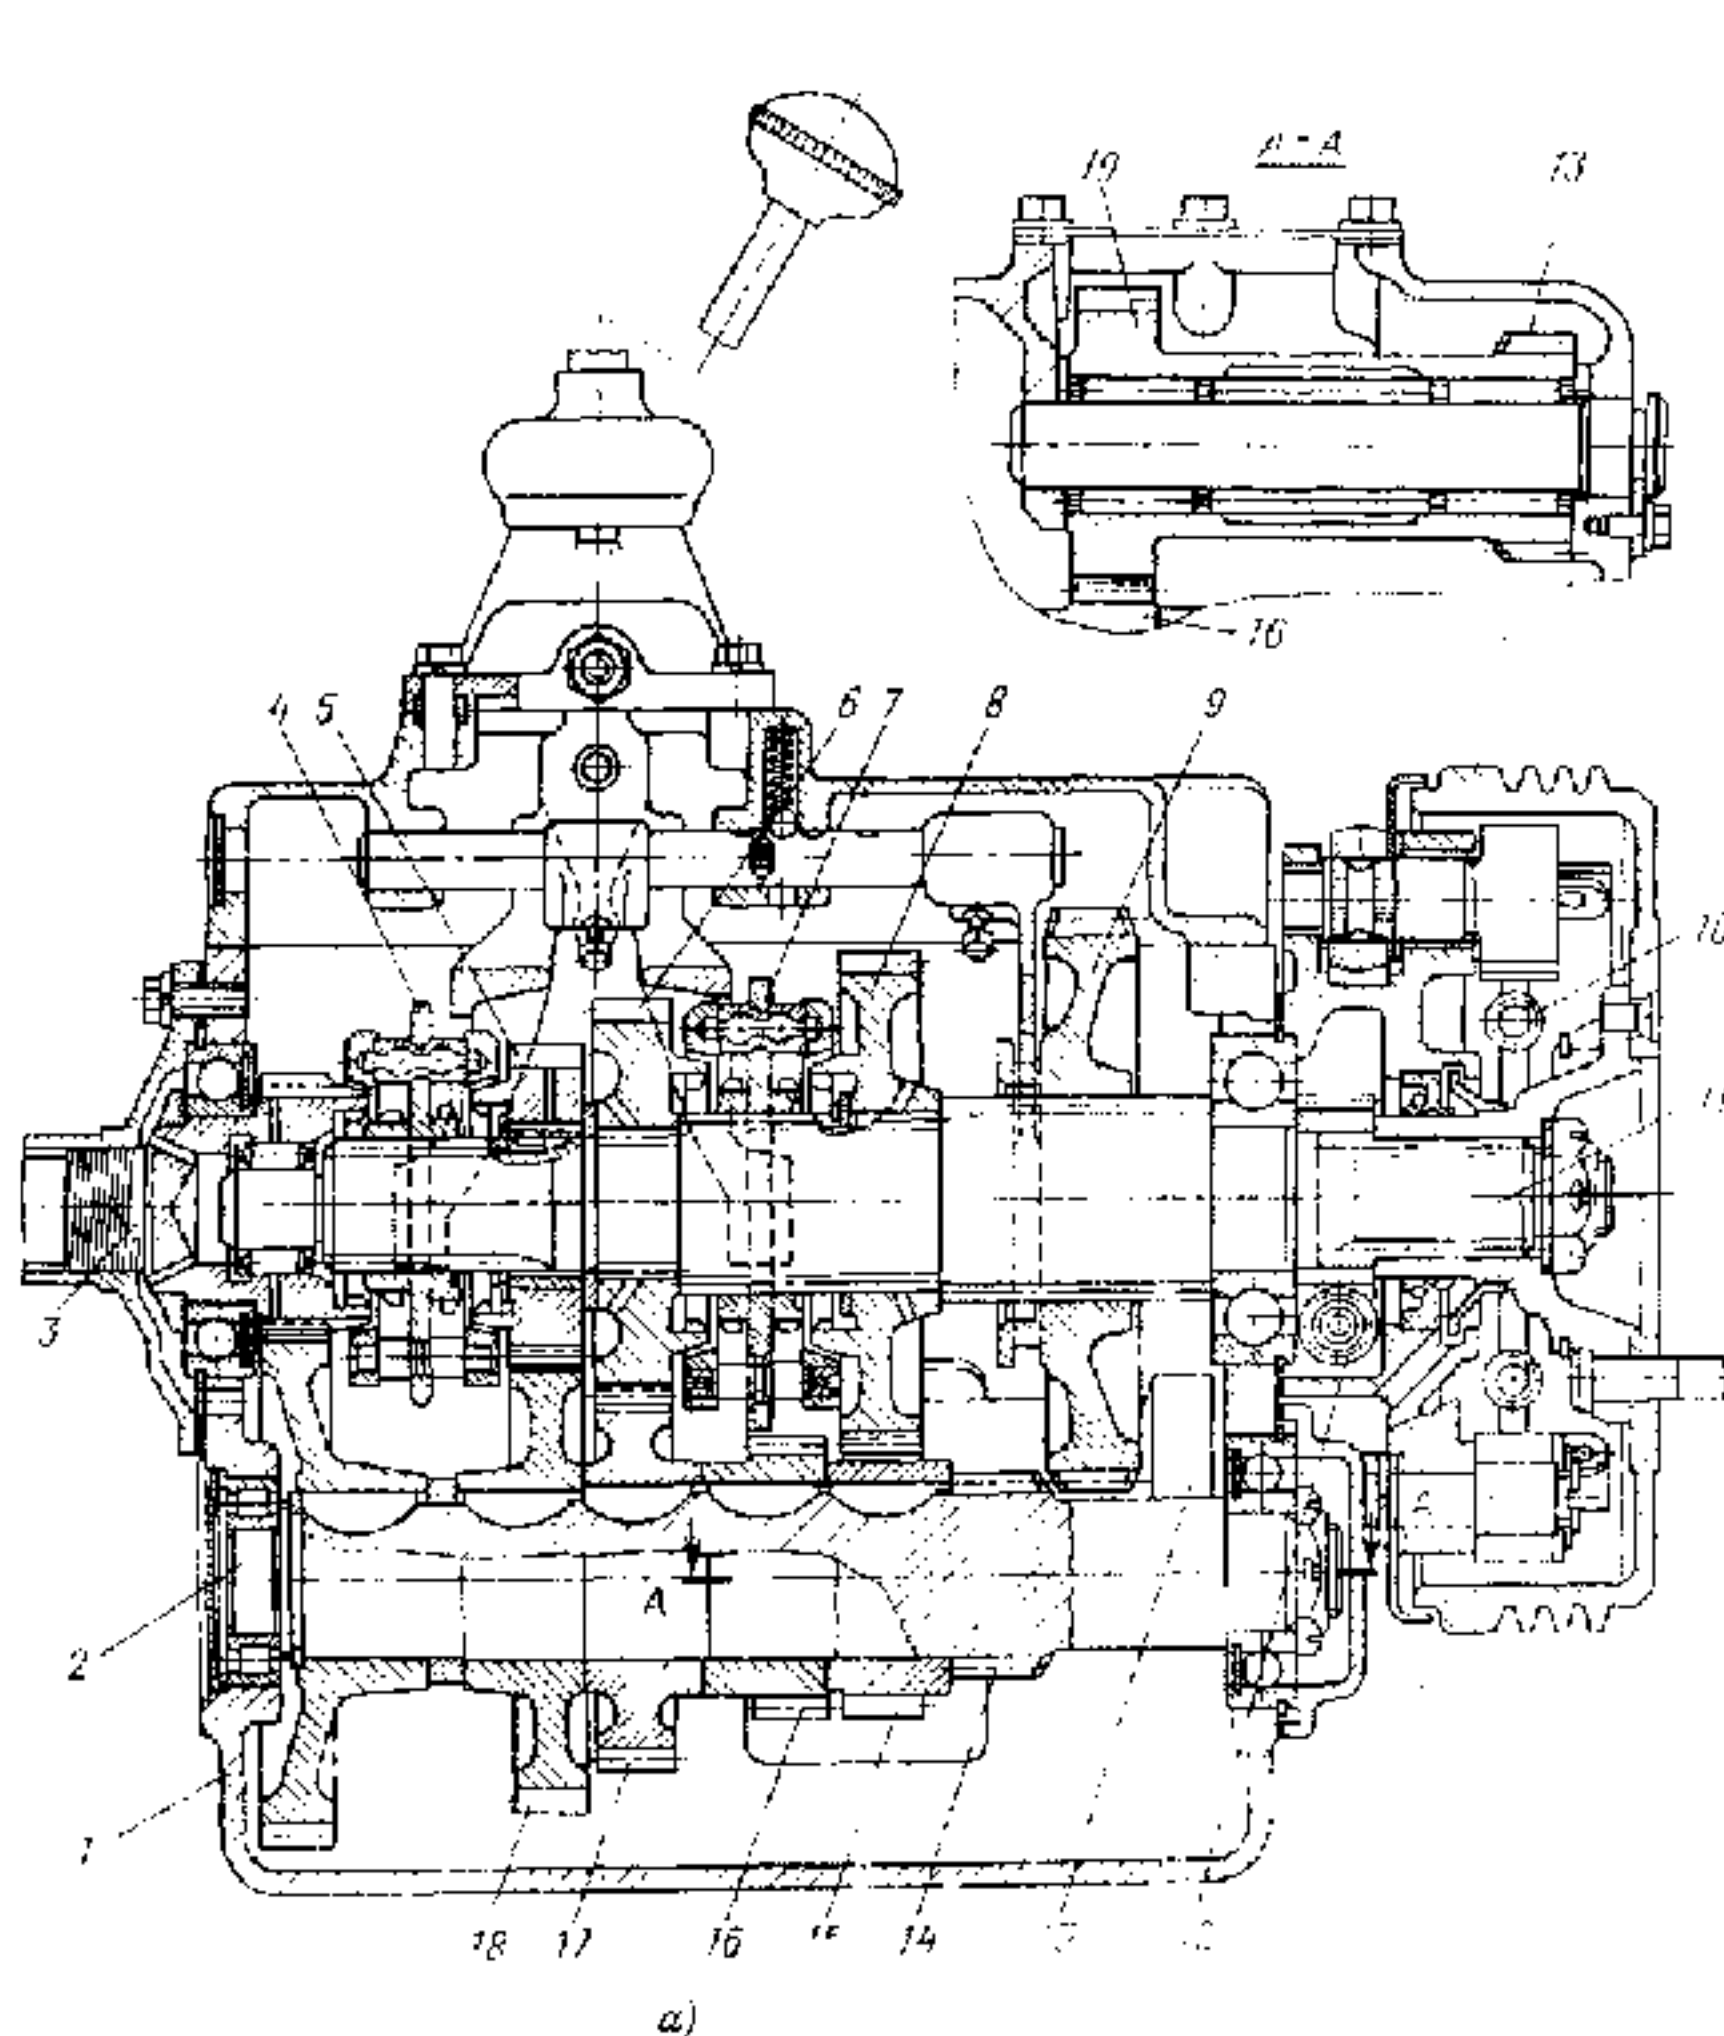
Коробка передач автомобиля ЗИЛ-130: а – общий вид; б –
